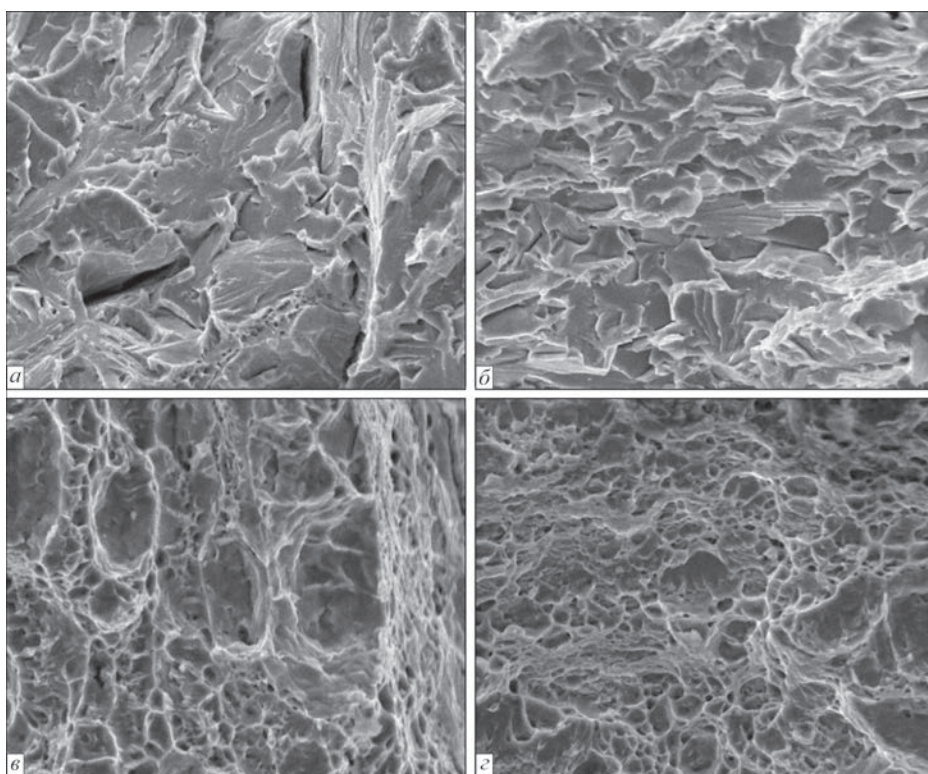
Характер разрушения в зоне магистральной трещины: а, б — хрупкий транскристаллитный скол в изломах образцов, изготовленных из сварного соединения (а), и обработанных методом ТЦС (б); в, г — вязкое разрушение образца из валиковой пробы (в) и основного металла (г), $\times 1550$
